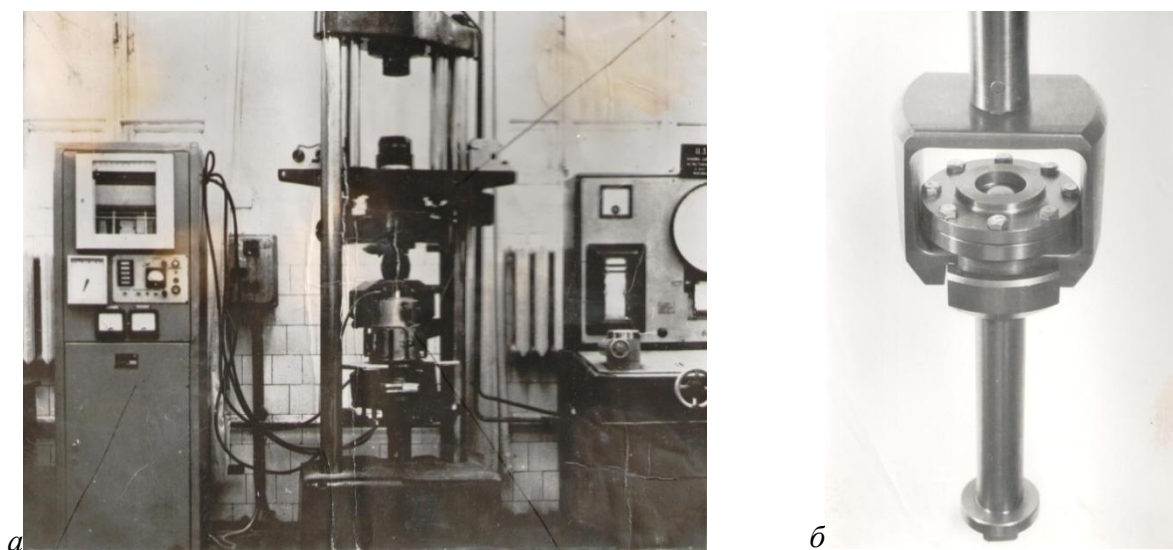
Испытание листового материала на двухосное растяжение методом выпучивания мембран на испытательной машине ЦДМУ-30:
